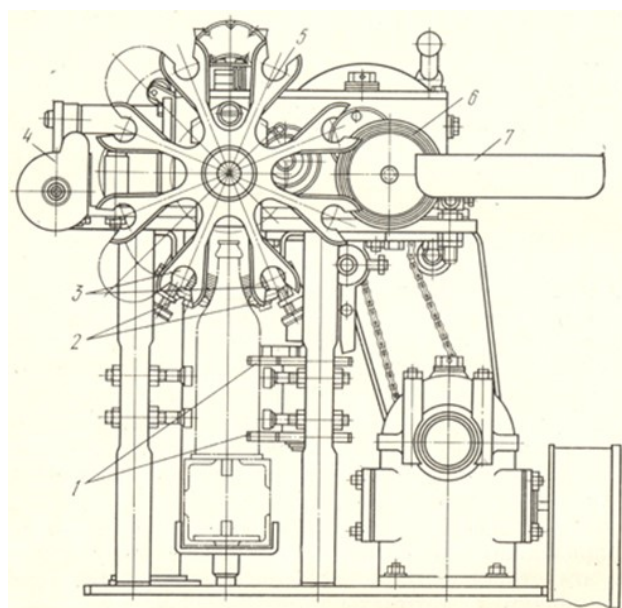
Автомат Б-12: 1 — направляючі; 2 — самоцентруючі ролики; 3 — щітки; 4 — датувальний пристрій; 5 — водила; 6 — чотирипазовий хрест; 7 — клеєва ванна.
